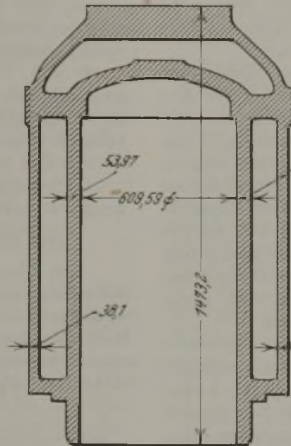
Deutscher Dieselmotorzylinder. Gewicht = 4573 kg.
